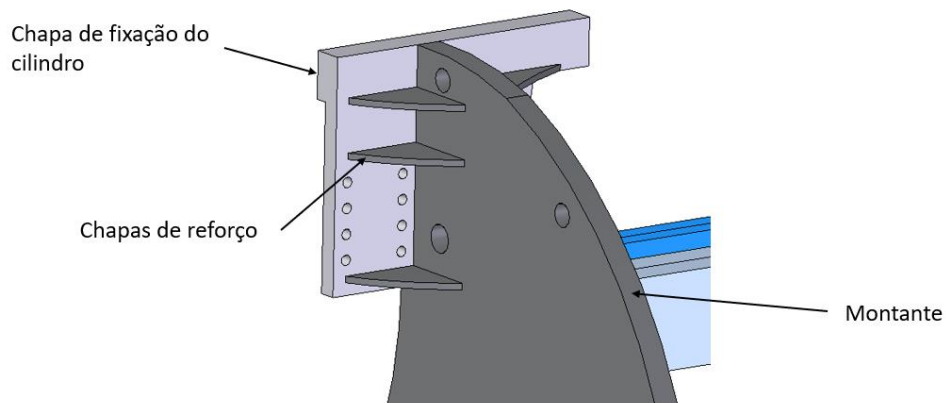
Geometria da zona posterior de fixação dos cilindros hidráulicos.
